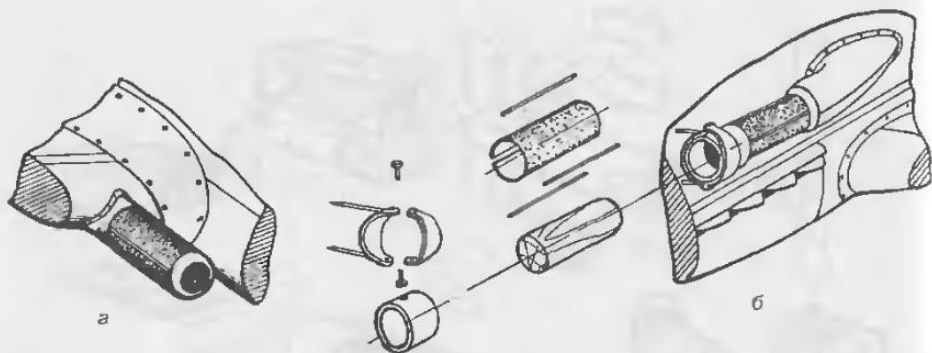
Пример изготовления воздухозаборников поршневых двигателей с противопыльными фильтрами: а - Ил-2 (СССР); б - Мессершмитт Ме-109 (Германия)
